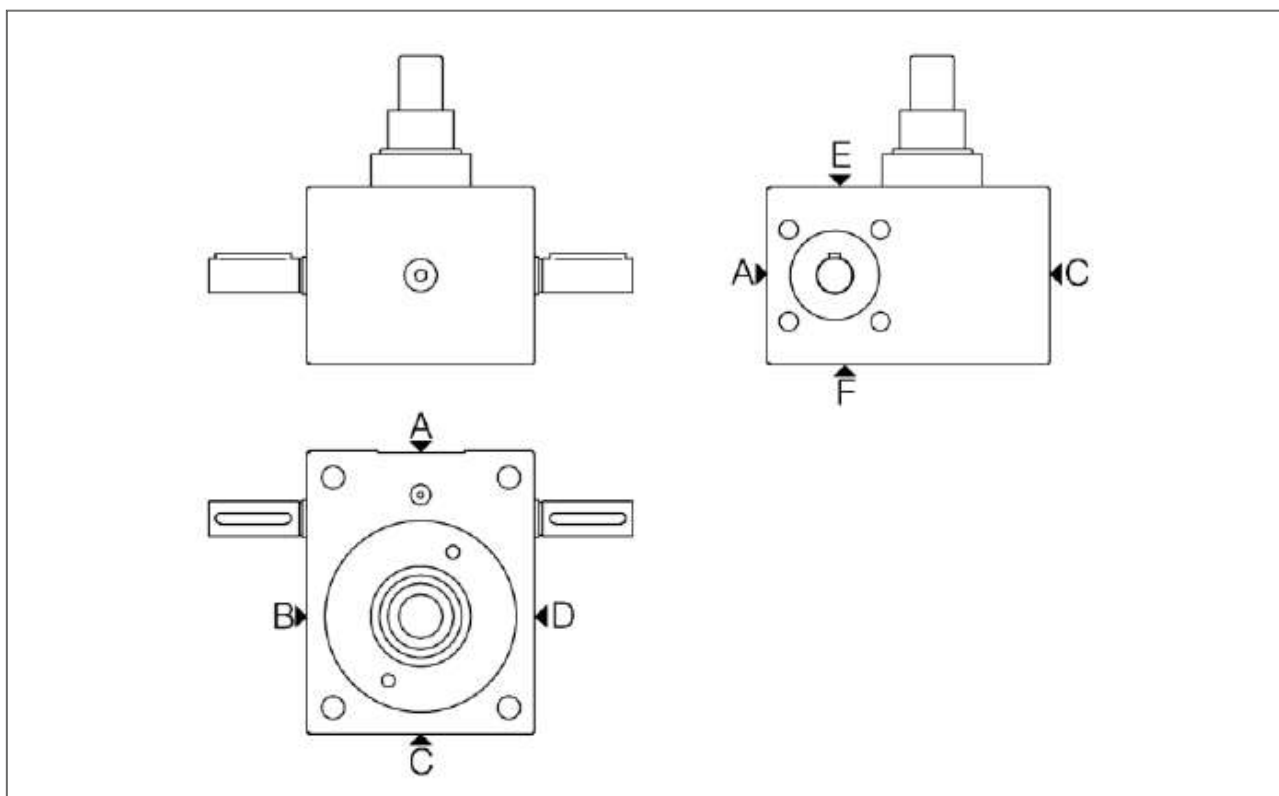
Vue d'ensemble du vérin de levage ZIMM
